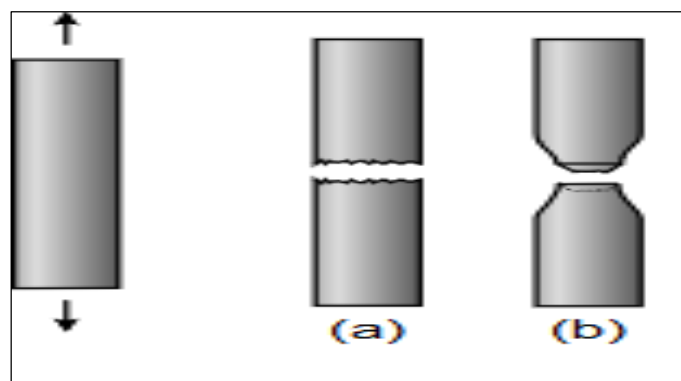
(a) Fractura Frágil, (b) Fractura Dúctil
